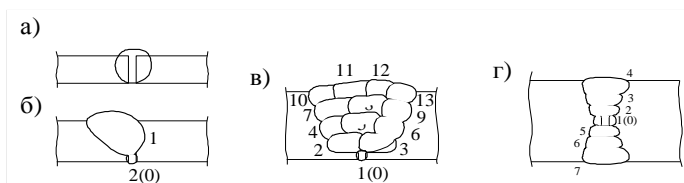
Поперечные сечения сварных швов (цифрами указана последовательность наплавки): а – однопроходный; б – однопроходный с подваркой корня; в – многопроходный; г – многослойный
